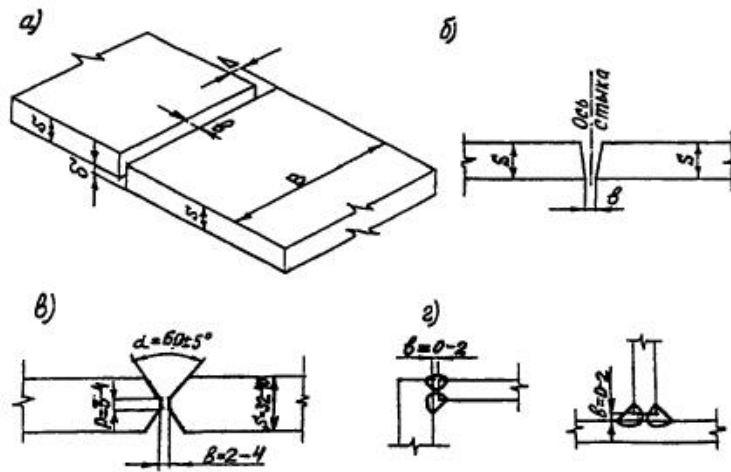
Допуски при сборке соединений под сварку
